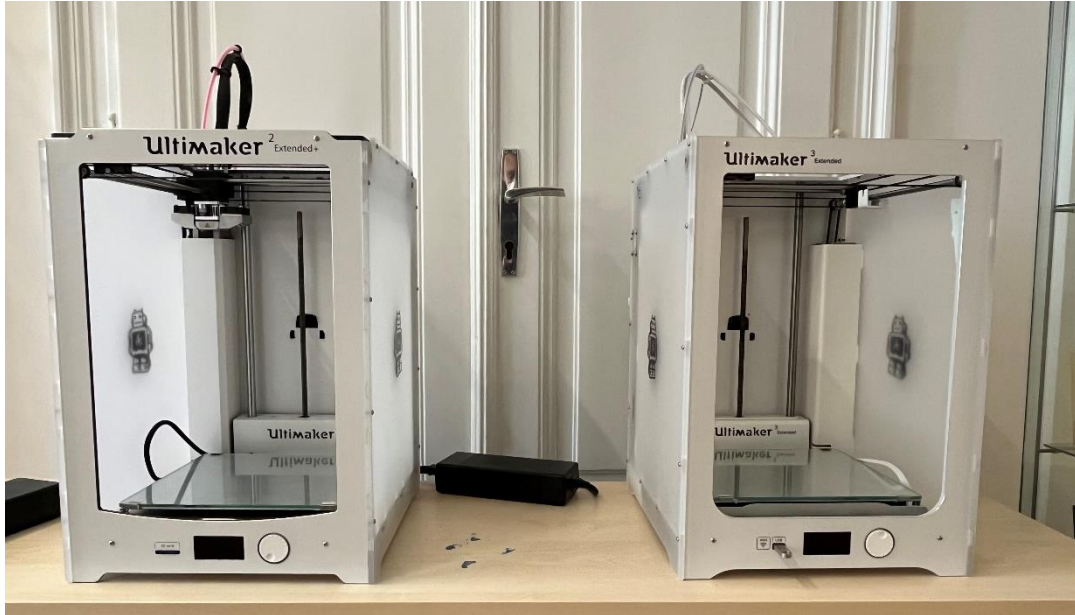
Impresoras 3D disponibles en la Universidad Técnica de Viena.
